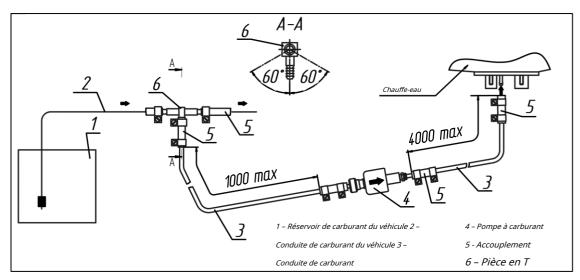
Aspiration du carburant à l'aide d'une pièce en T
